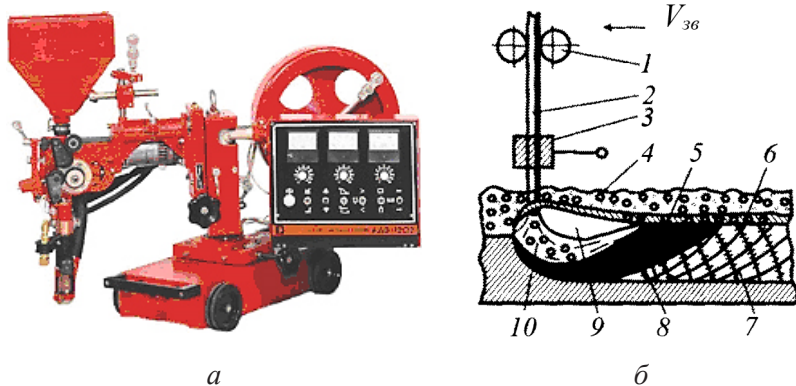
Зовнішній вигляд автомата АДФ-1202 (а) та схема процесу автоматичного дугового зварювання під флюсом (б)
